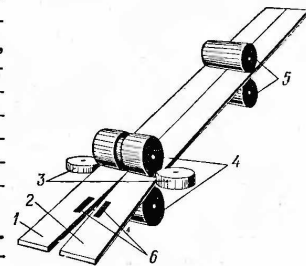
Принципиальная схема сварки биметаллических полос
